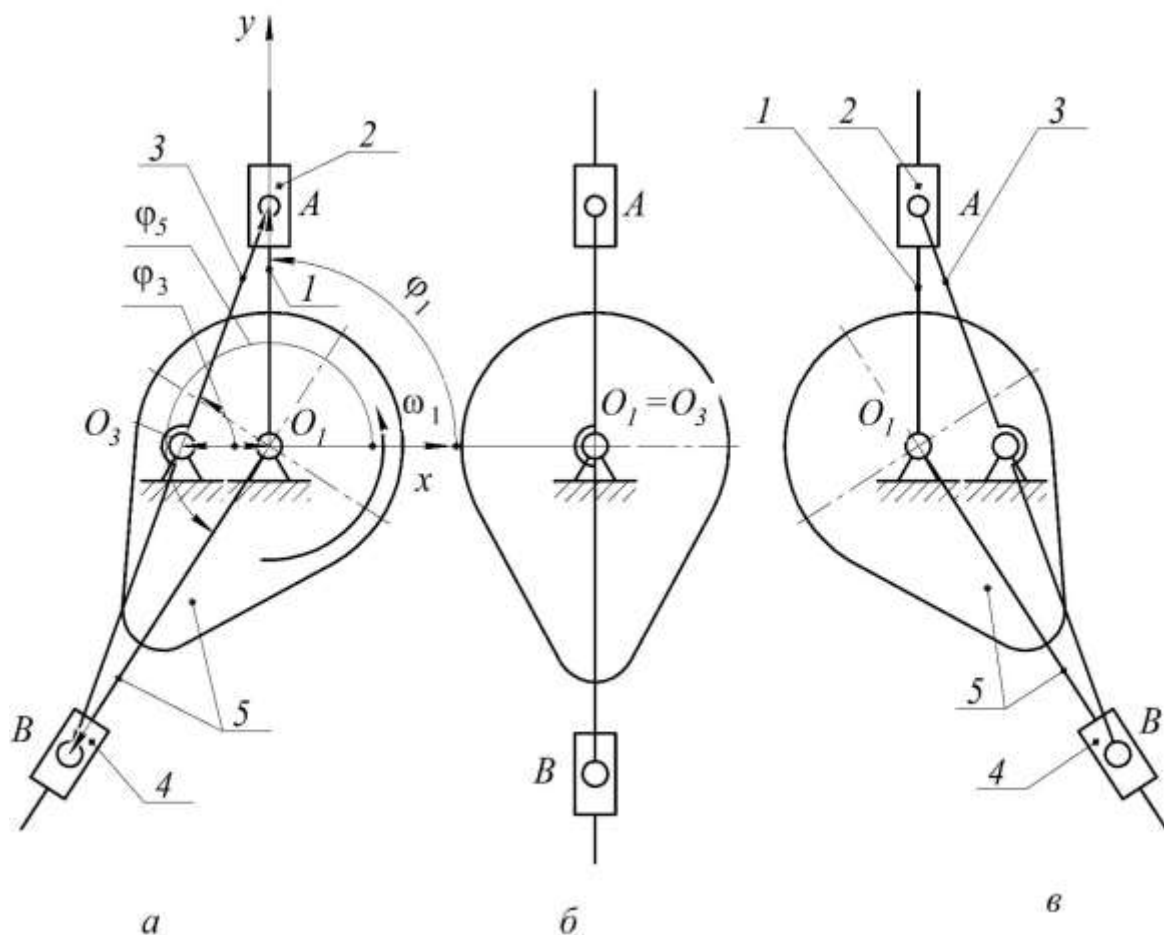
Кинематическая схема двойного кулисного механизма передачи движения от распредвала к кулачку:
